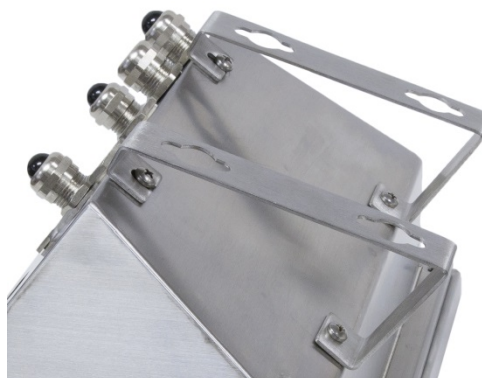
Fixação das Braçadeiras de Montagem na Parede
